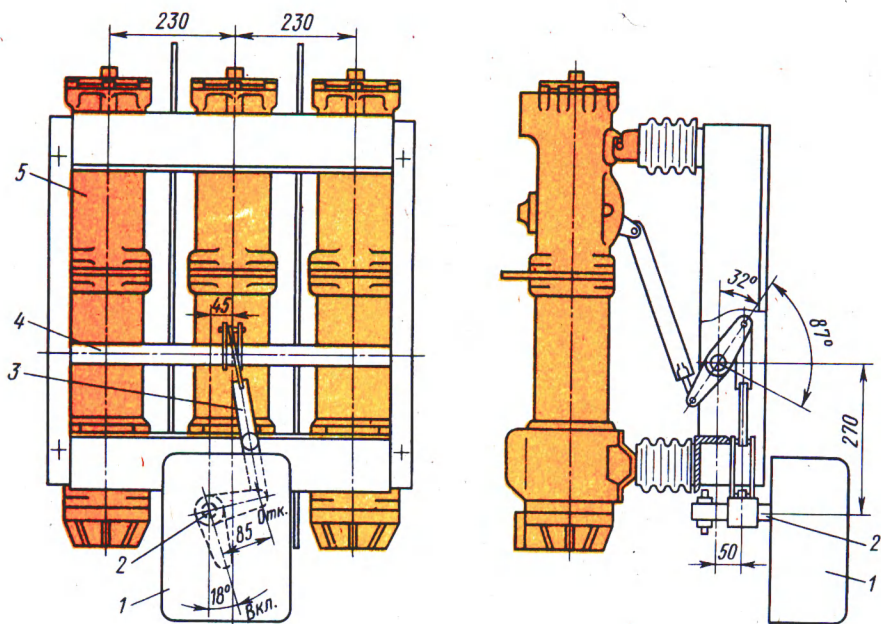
Установочный чертеж масляного выключателя ВМП с приводом ПЭ-11 в шкафу КРУ
